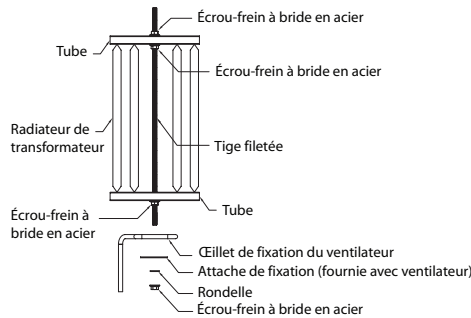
Pose du nécessaire de fixation Guard-Mounting (vue de dessus)
